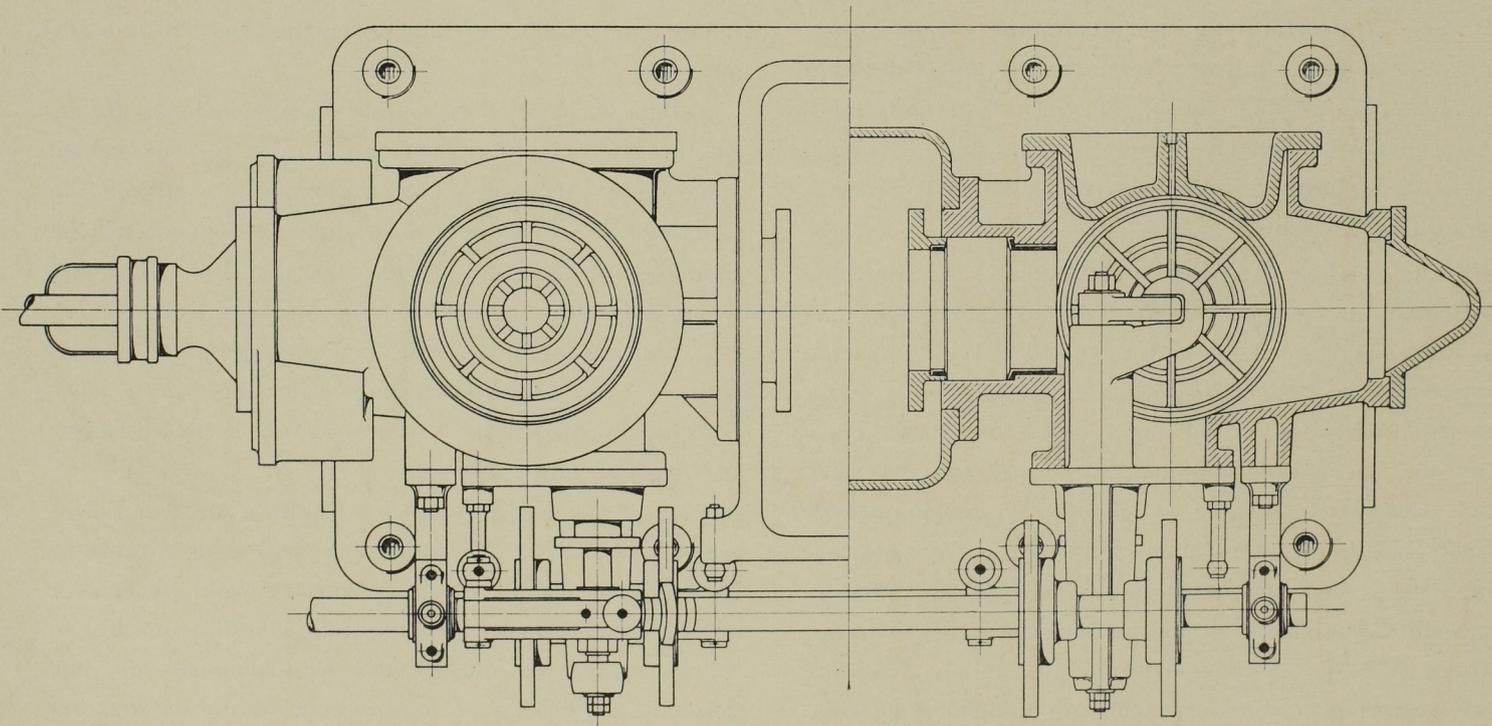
Grundriss der Pumpe. Masst. 1 : 15.
